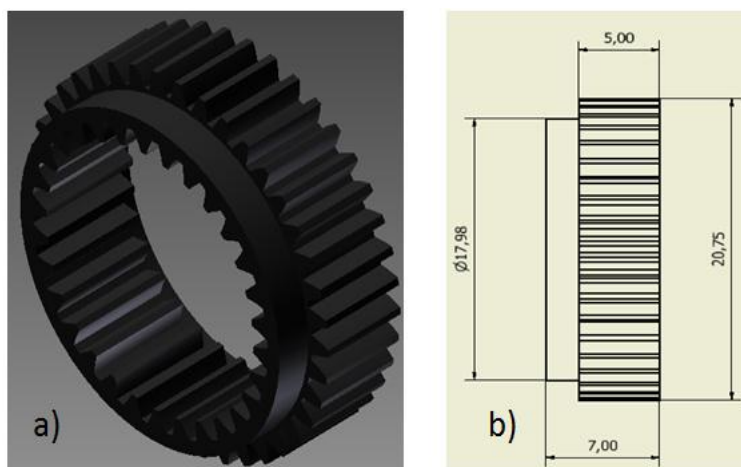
Engrane móvil. a) Vista isométrica b) Vista lateral acotada
